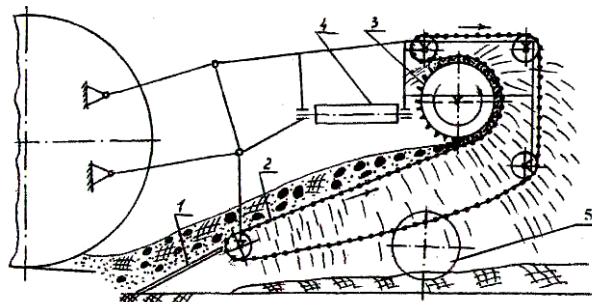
Конструктивная схема экспериментальной машины при подготовке почвы 1-лемех, 2-прутковый элеватор, 3-рыхлительный барабан, 4-ноперечный транспортер, 5-колесо.
